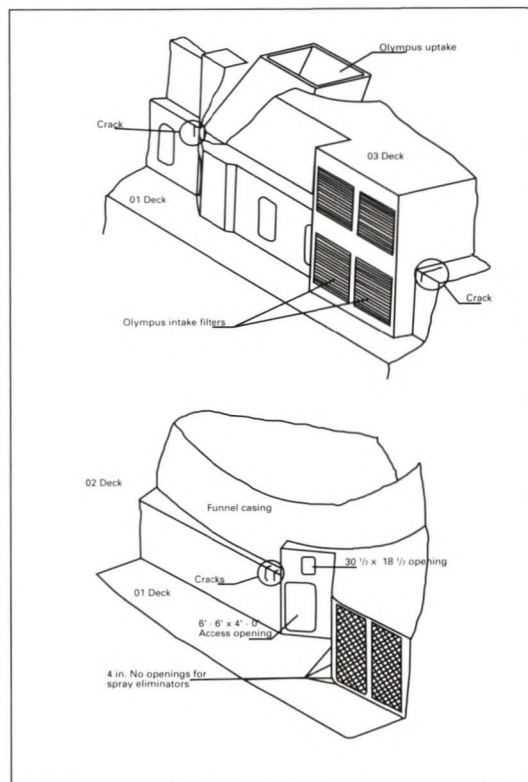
y 10: Agrietamiento en superestructura en destructores tipo 42.
